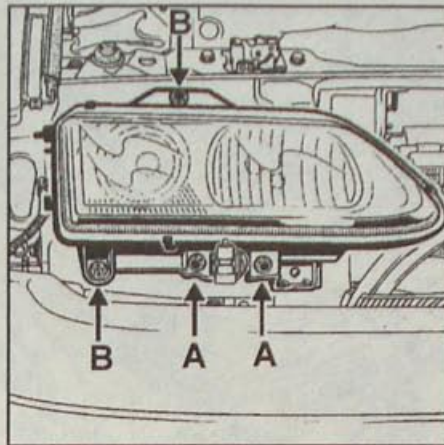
Расположение болтов (A) крепления омывателя фар и гаек (B) крепления блок-фар
